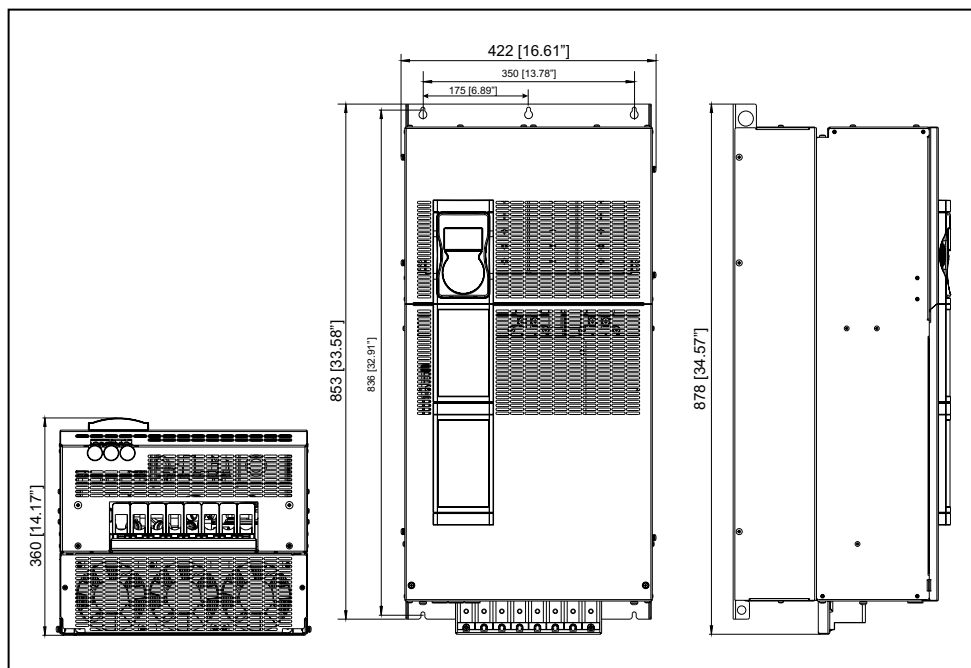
Размеры для типоразмера 6 (ADV200-...-4)
